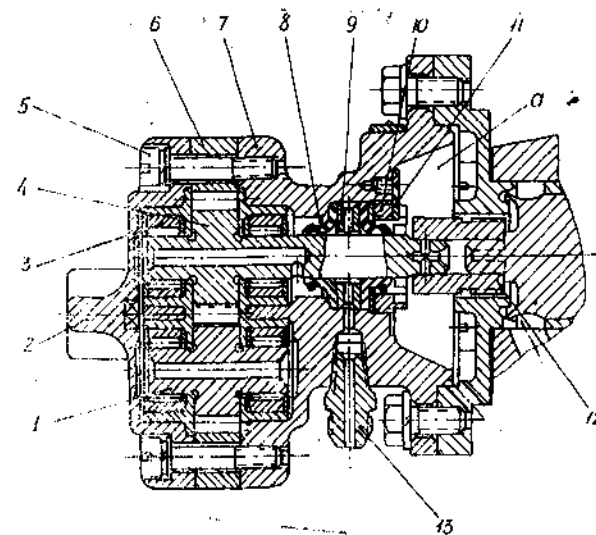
Топливоподкачивающий насос: 1—ведомая шестерня; 2—крышка; 3—подшипник; 4—ведущая шестерня; 5—винт; 6—корпус; 7—кронштейн; 8—сальник; 9—дренажное кольцо; 10—гайка; 11—стопорная планка; 12—муфта; 13—штуцер
